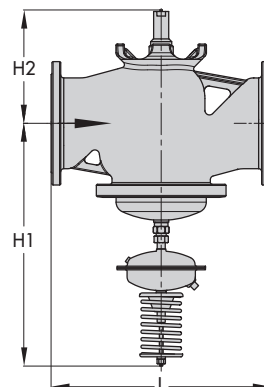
· Dimensioni di valvole bilanciate e regolatori
